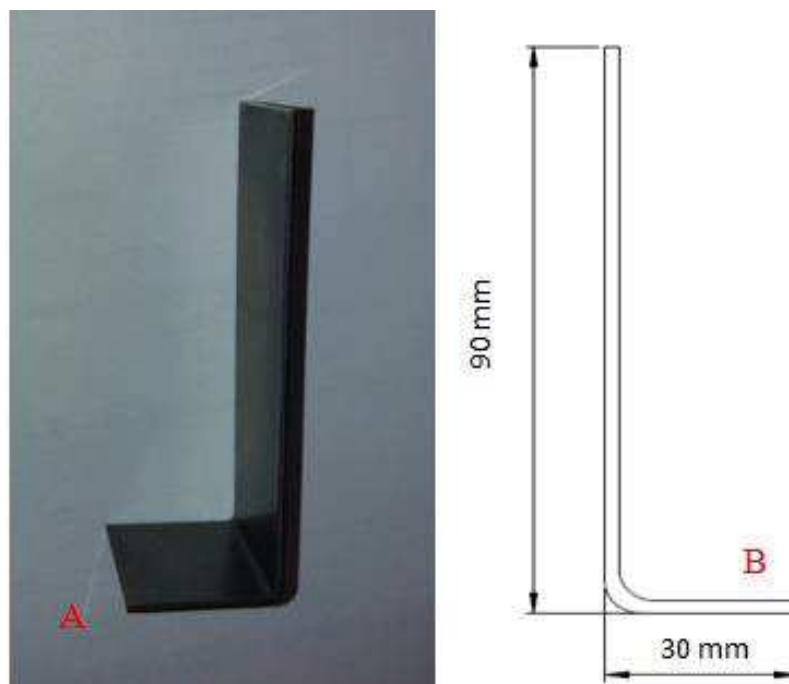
(A) Pièce après pliage (B) dessin de définition.
